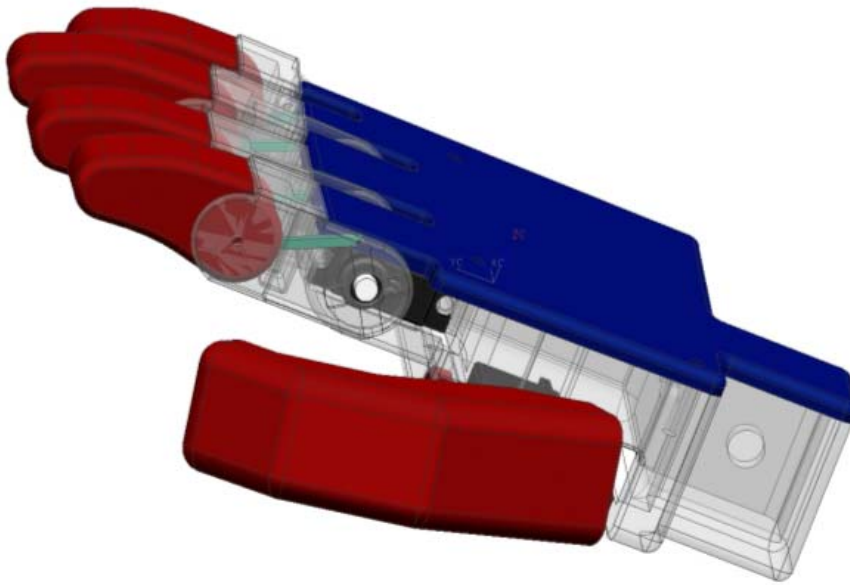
Vista isométrica del prototipo final en CAD
